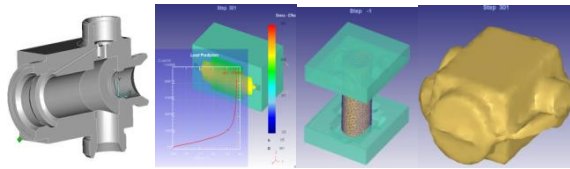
Модель детали, анализ процесса прессования, модель заготовки
